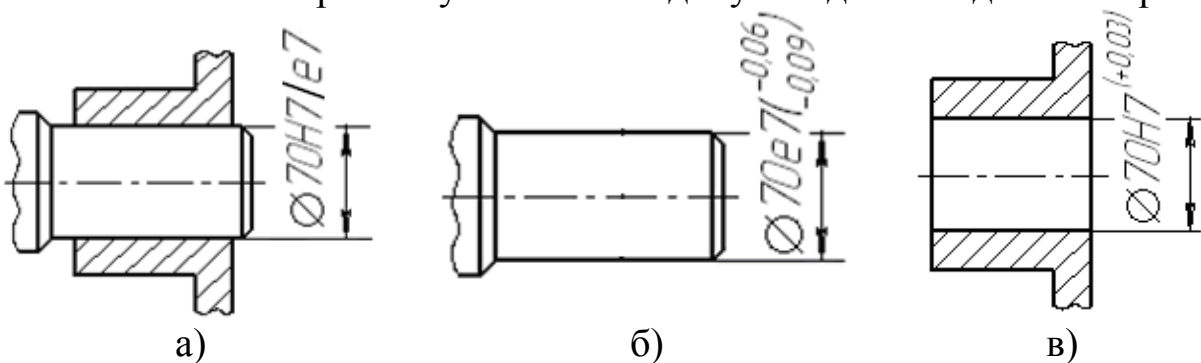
Ескізи з'єднання (а), вала (б) та отвору (в) на робочих креслениках деталей
